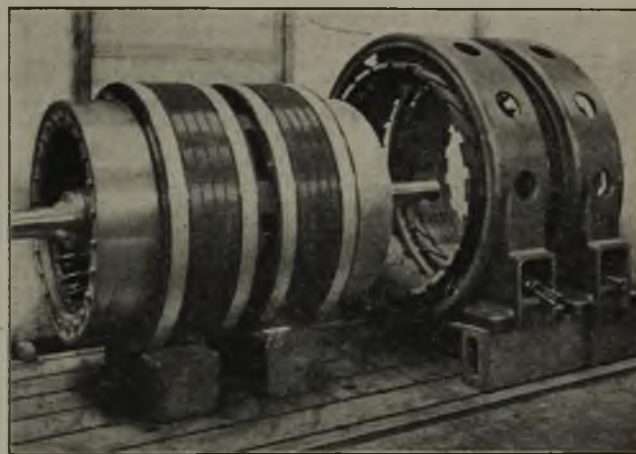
Rotor und Stator eines Doppelkollektormotors der A. G. Brown, Boveri & Co.
